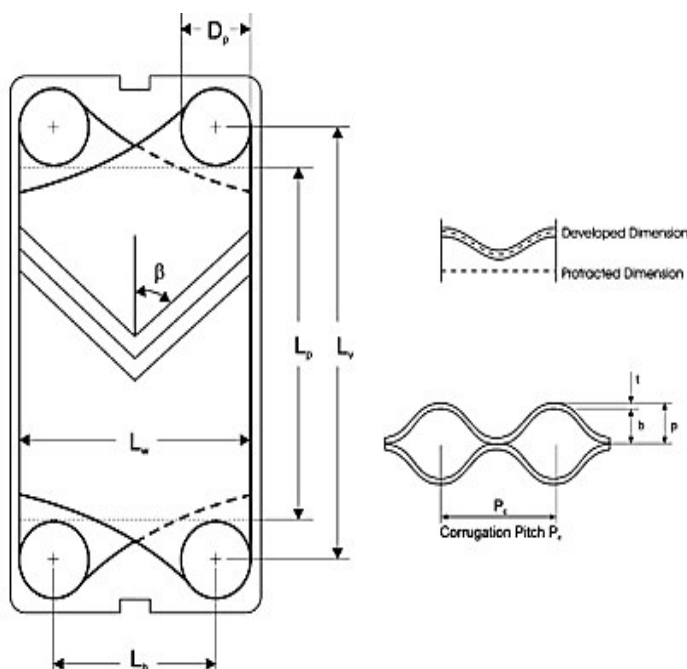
Dimensiones geométricas del intercambiador de placas [6].
